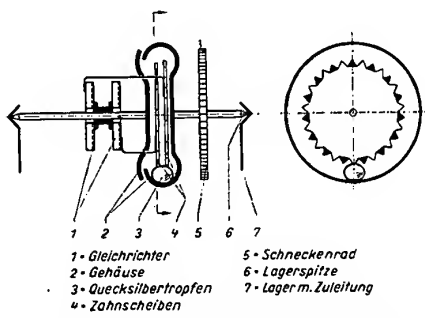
Quecksilber-Kontaktdose als Umschalter mit Gleichrichterplatten
